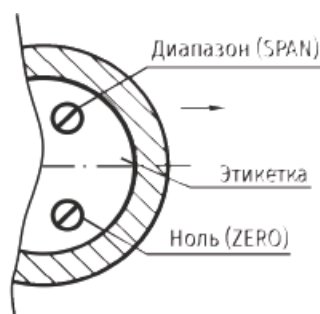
Схема расположения корректоров НОЛЬ и ДИАПАЗОН
